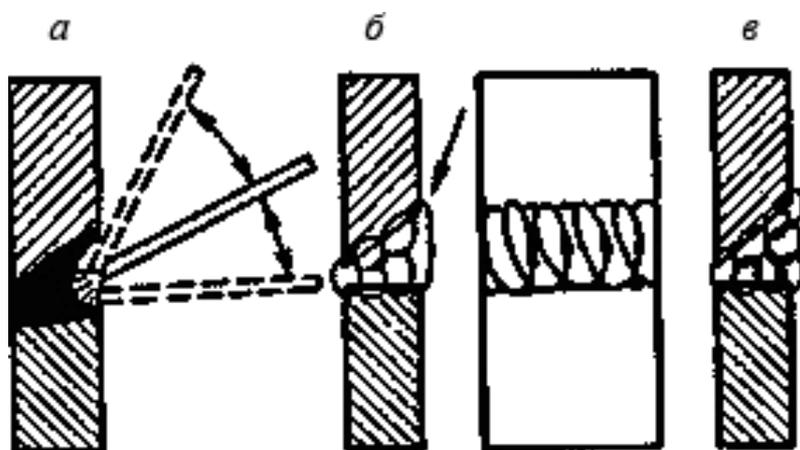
Сварка горизонтальных швов:
